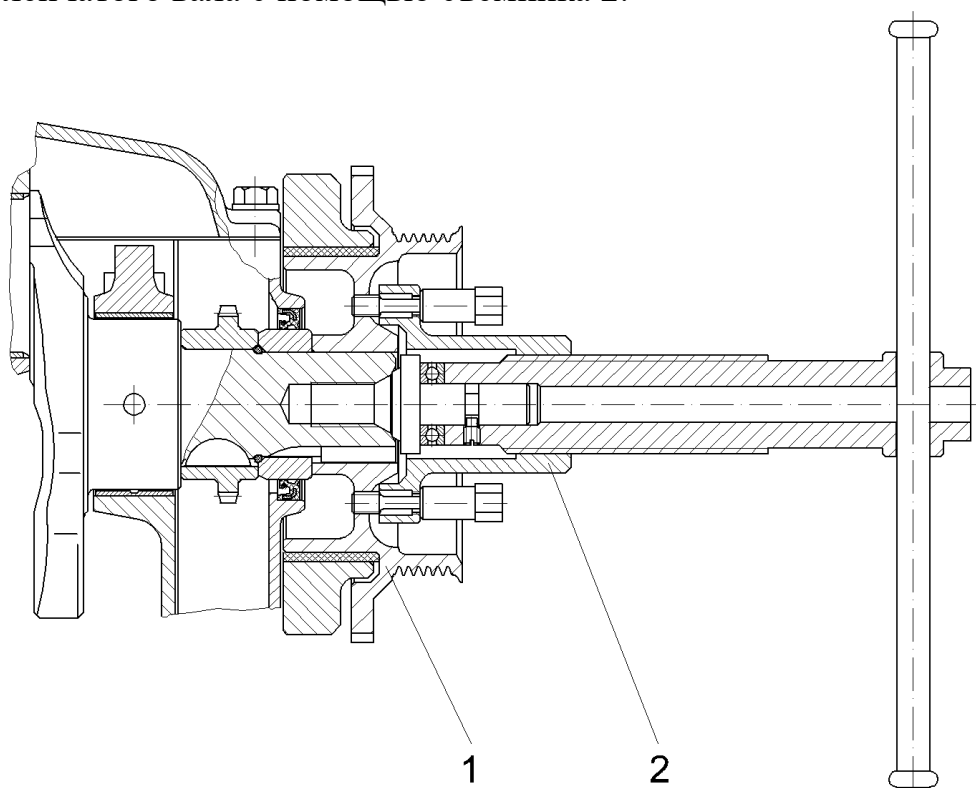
Снятие шкива коленчатого вала с помощью съёмника:
